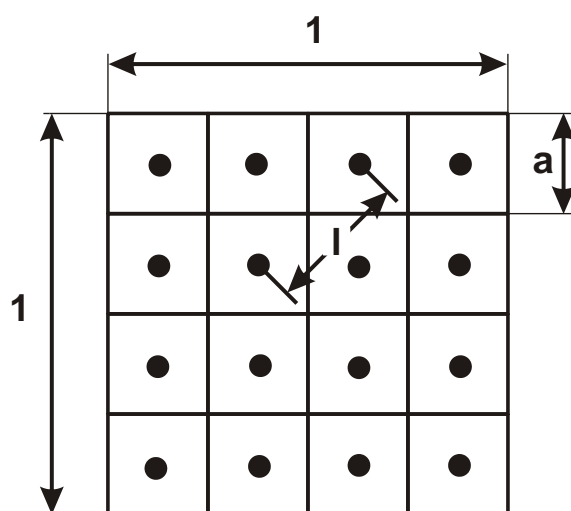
Розрахункова схема поверхневої концентрації зерен на робочій поверхні круга
